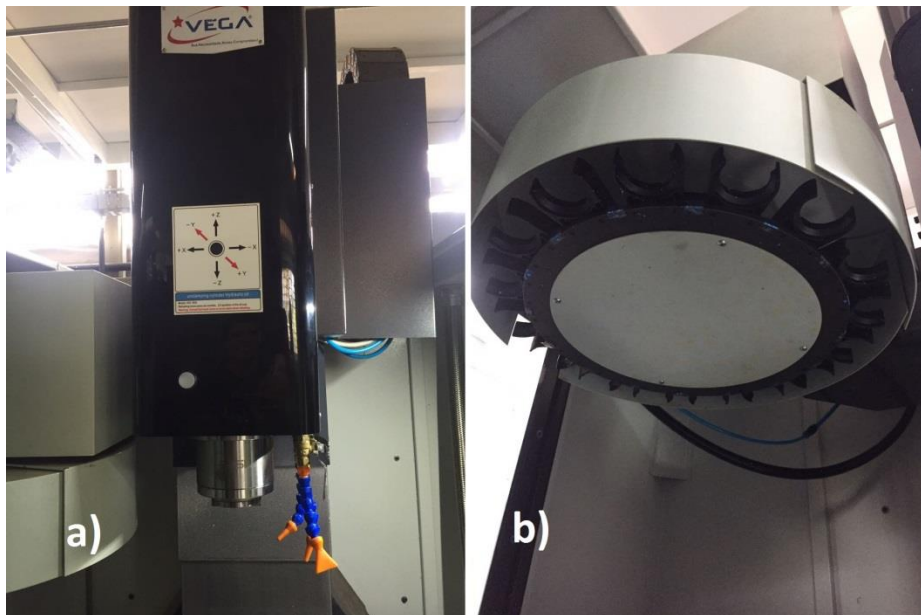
Componentes principais: a) Cabeçote; b) Magazine de ferramentas
